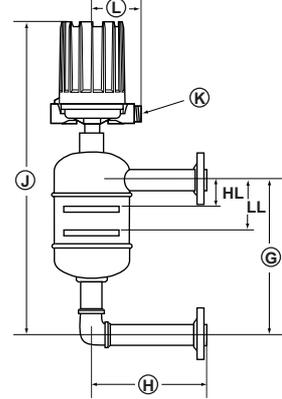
B75 mit Gewinde oder Schweißnippel Ausführung oben seitlich/unten
